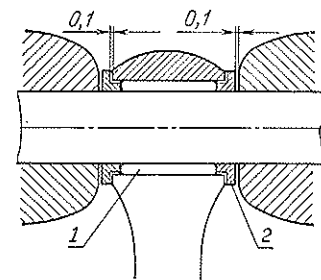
Игольчатый подшипник верхней головки шатуна: 1 — иголки 1,5 × 20; 2 — шайба (сталь 45, вальт НRC 40—45).
